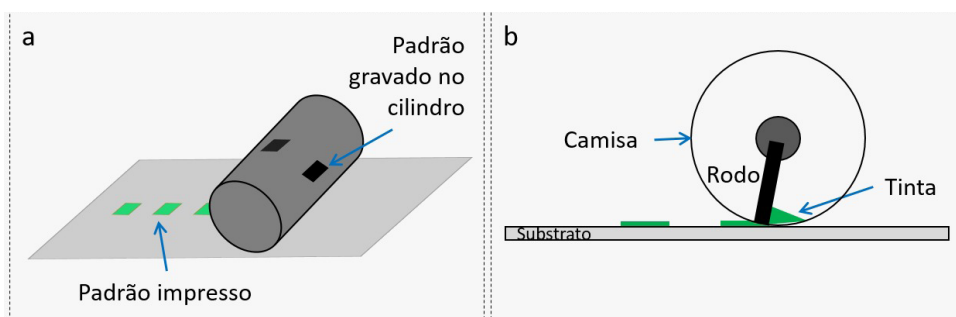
Serigrafia rotativa. a) Representação do processo de impressão; e b) Corte transversal do cilindro de impressão em que aparece a posição do rodo de raspagem de tinta e camisa de impressão do padrão.
